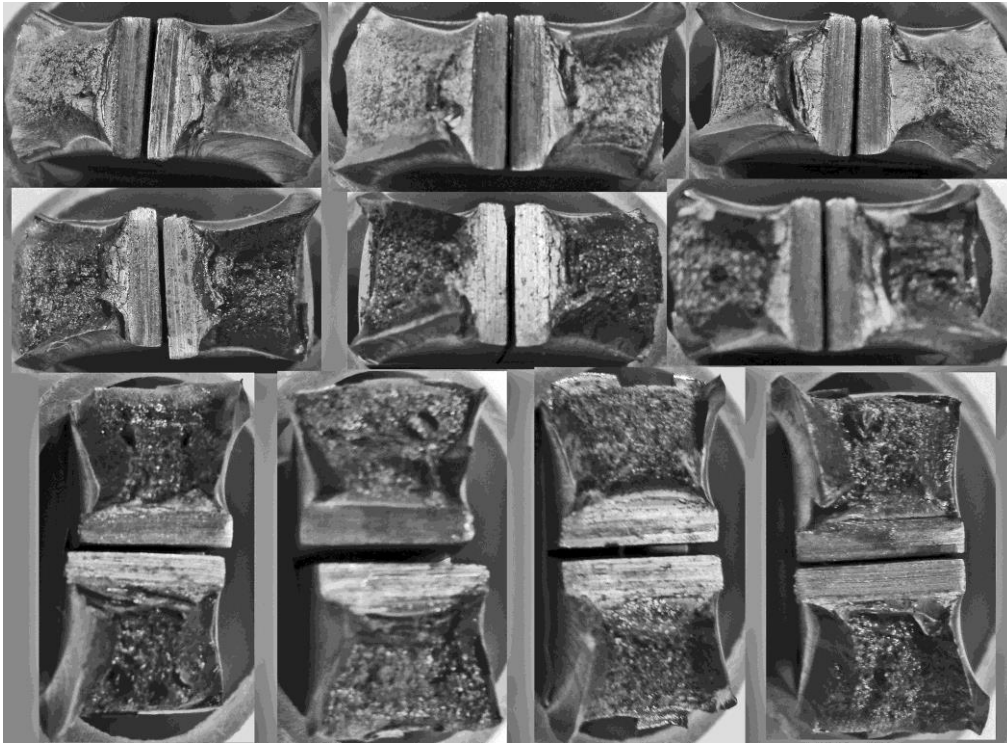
Fotografias das superfícies de fratura do ensaio Charpy-V, dos corpos de prova soldados com 200 °C de pré-aquecimento.
